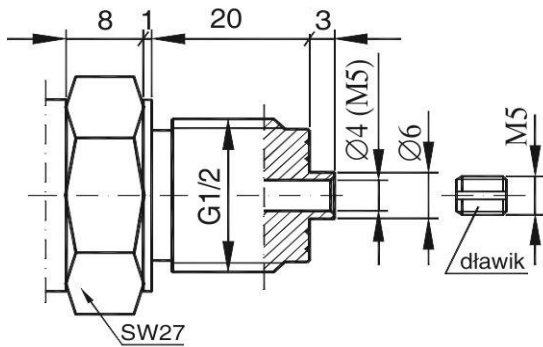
а. Штуцер типа G1/2 с резьбой G1/2"
